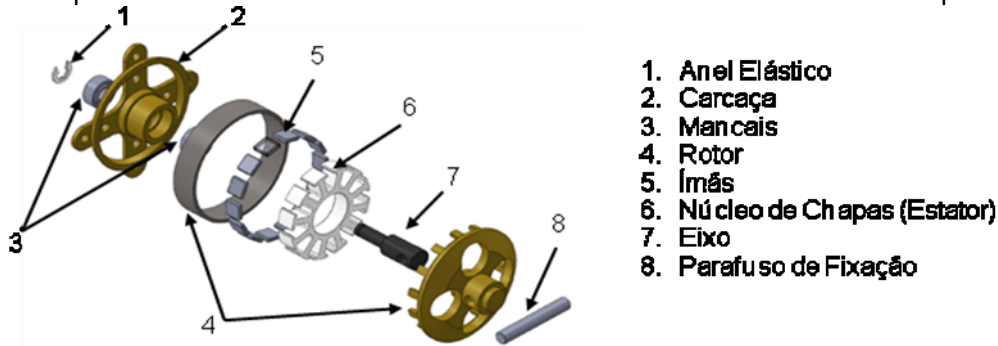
Motor Trifásico de Ímãs Permanentes em Vista Explodida
